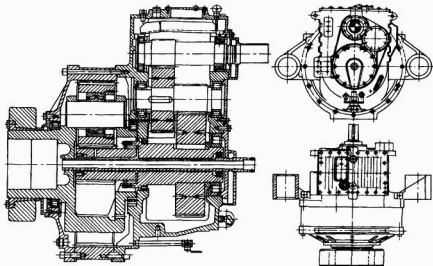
一级行星齿轮和两级平行轴齿轮传动组成的典型齿轮箱结构
